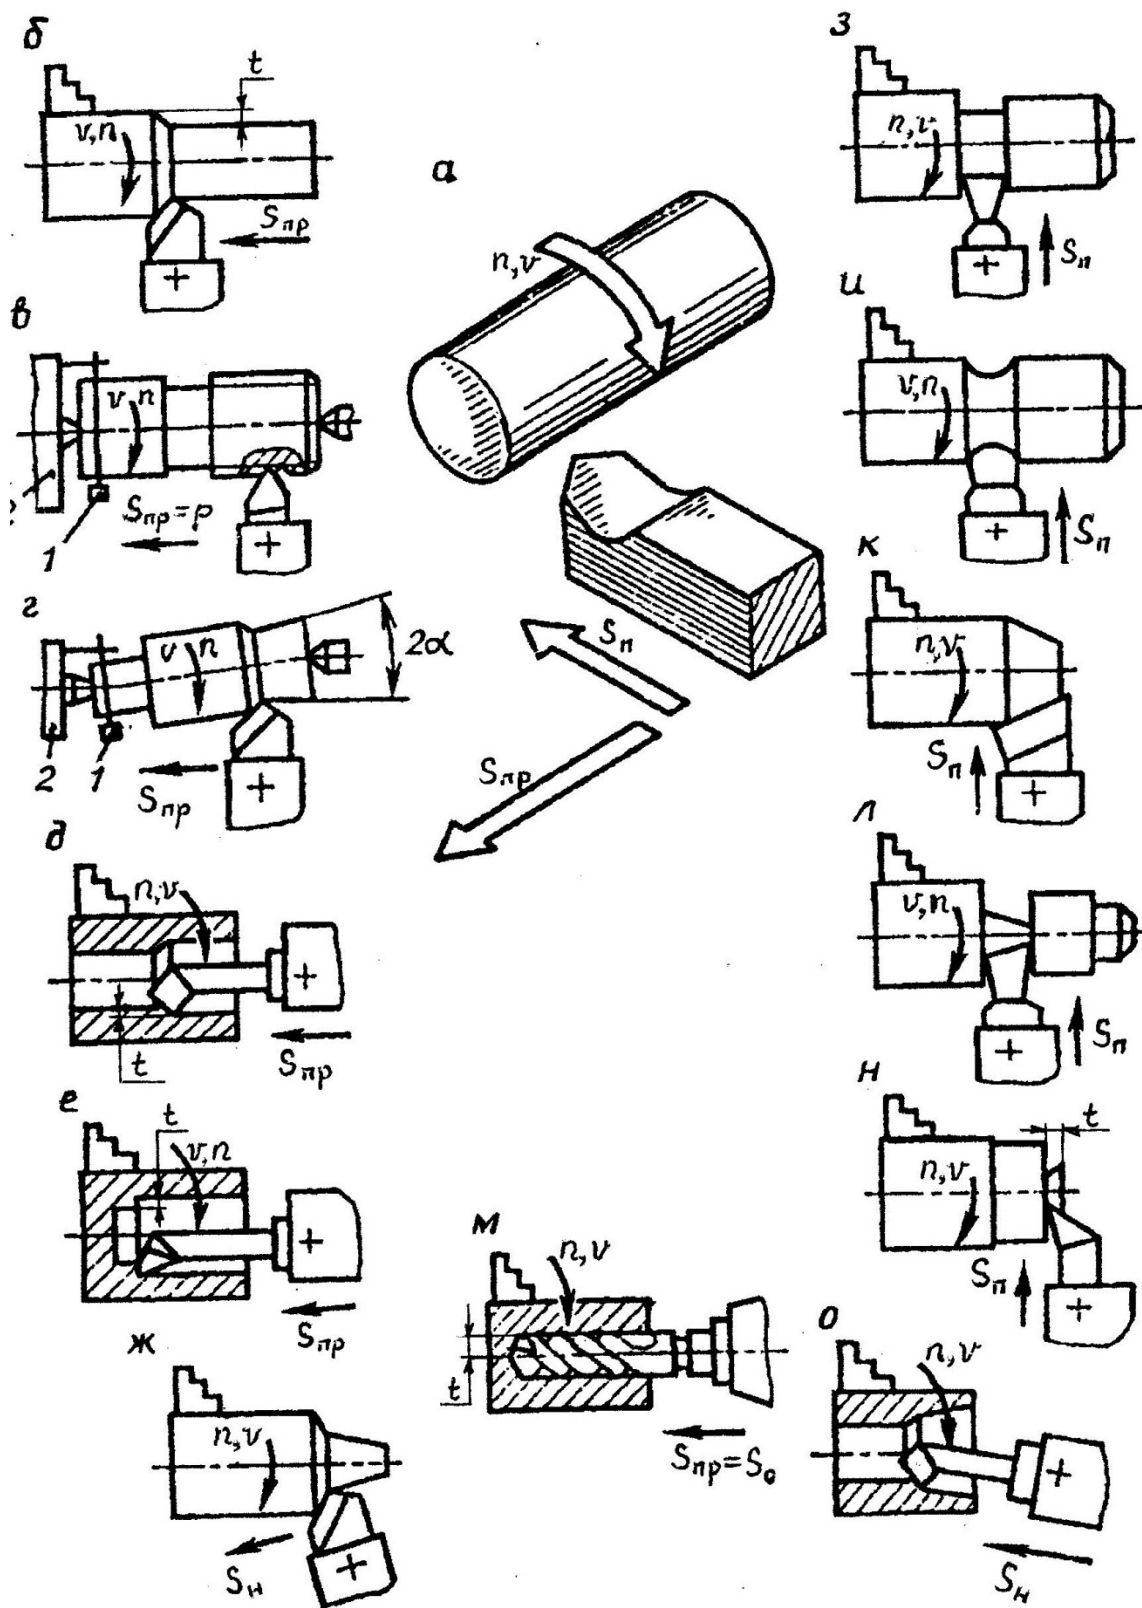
Совмещенные с установкой схемы обработки заготовок на токарных станках: а – положение заготовки и инструмента и параметры режима обработки; б – обработка наружной цилиндрической поверхности за-
